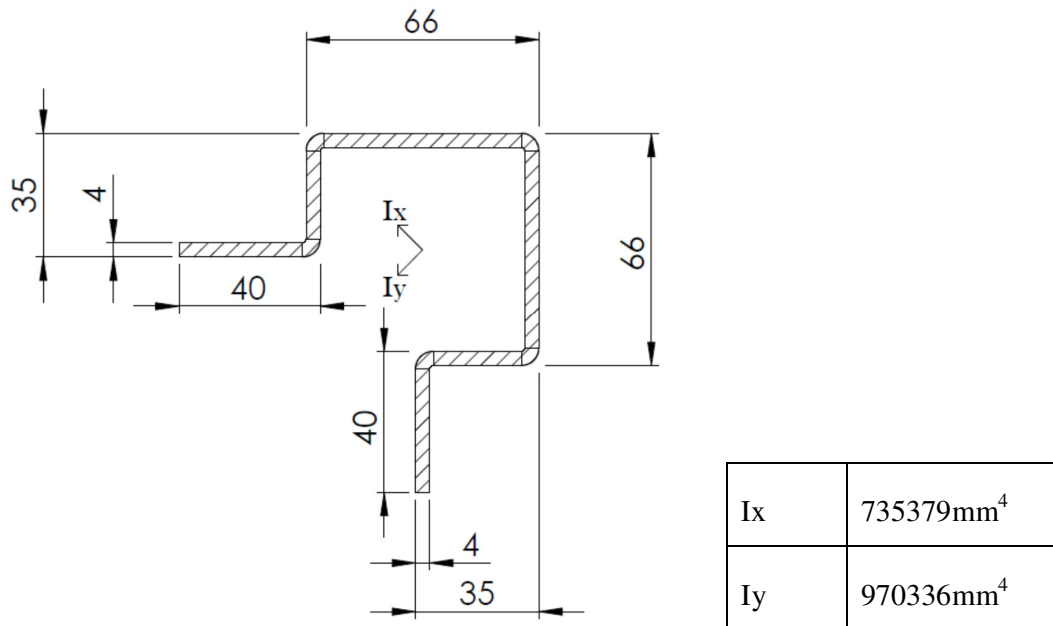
Secção transversal do pilar utilizado na estrutura autoportante dos *homelift* GRUPNOR® e objeto de estudo neste trabalho.
